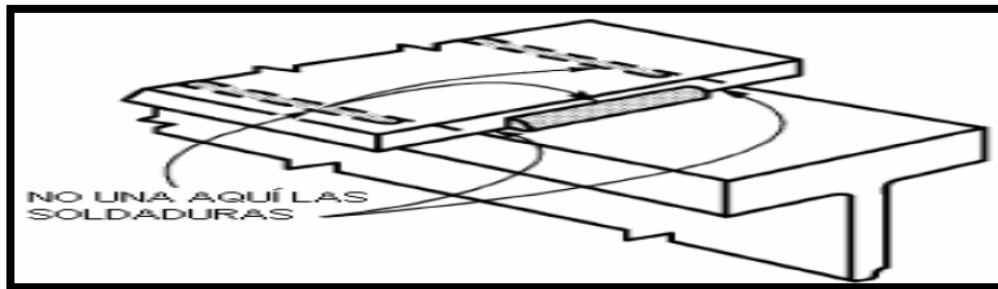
Soldadura de filete en lados opuestos de un plano común
